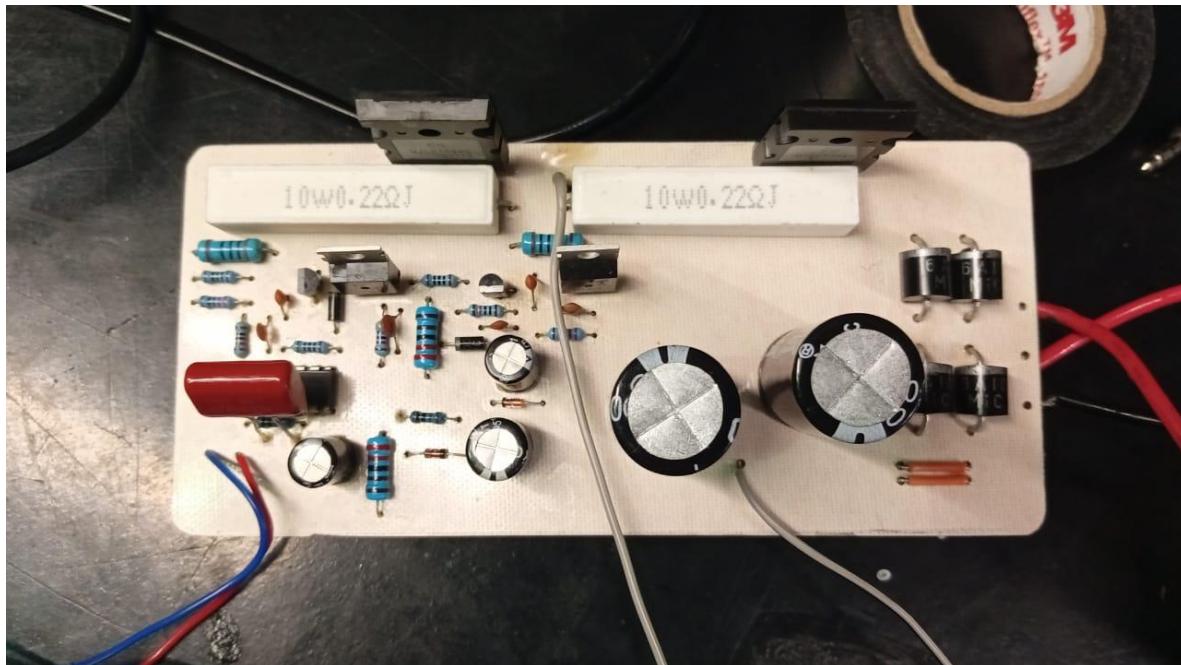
Quinto grupo de componentes soldados, junto a la bocina, auxiliar y transformador.
